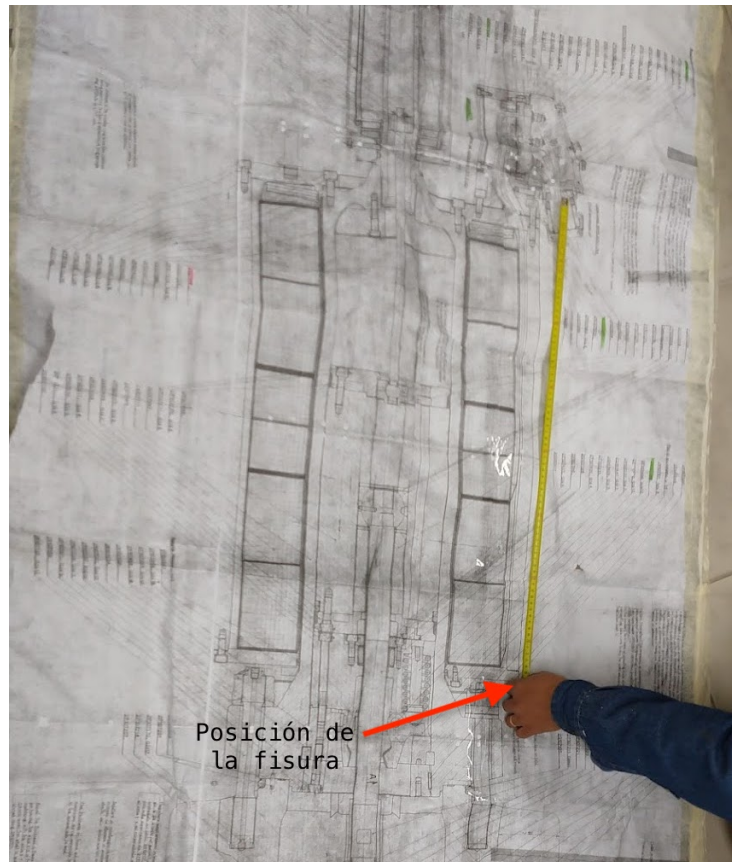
Ubicación de la fisura en el plano a escala 1:1 de la válvula.
